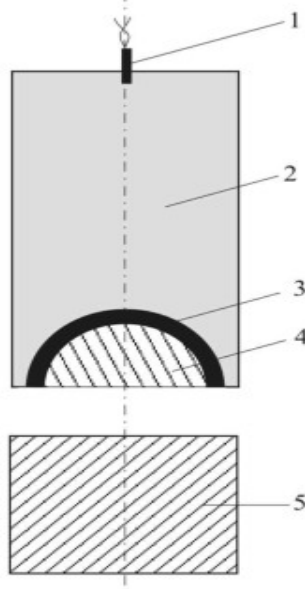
Схема вибухового генератора плазмових струменів: 1 – електродетонатор; 2 – вибухова речовина; 3 – пластина-ударник; 4 – конічна виїмка; 5 – сталеві матриця./ Scheme of an explosive generator of plasma jet: 1 – electrical detonator; 2 – explosive substance; 3 – drum plate; 4 – conical groove; 5 – steel matrix.
